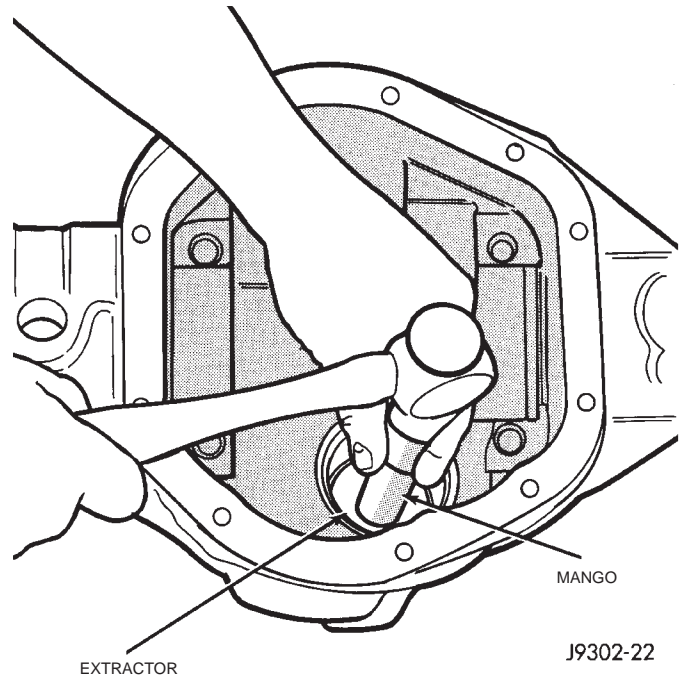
Desmontaje de la cubeta del cojinete delantero
